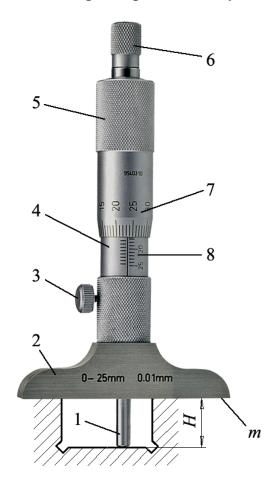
Глубиномер микрометрический ГМ-25: 1 — измерительный стержень; 2 — основание (траверса); 3 — зажим микрометрического винта; 4 — стебель; 5 — барабан; 6 — механизм трещотки; 7 — шкала барабана; 8 — шкала стебля
